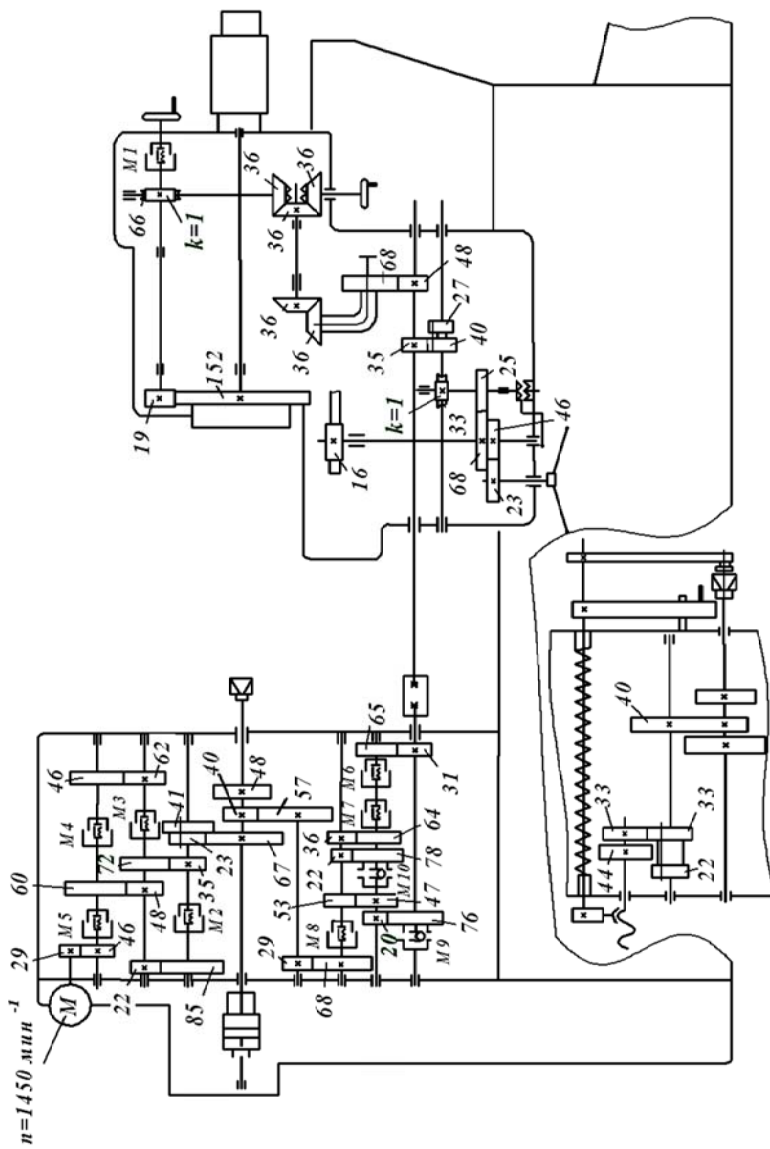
Кинематическая схема токарно-револьверного станка модели 1К341
